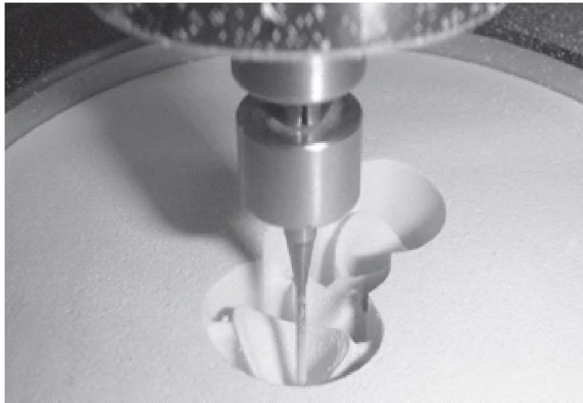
Етапи виготовлення ортопедичних конструкцій за допомогою фрезерувального апарата.
